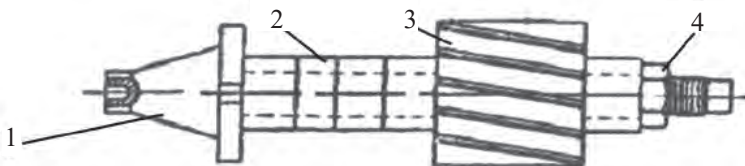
Оправка: 1 – конус; 2 – установочное кольцо; 3 – фреза; 4 – гайка.
